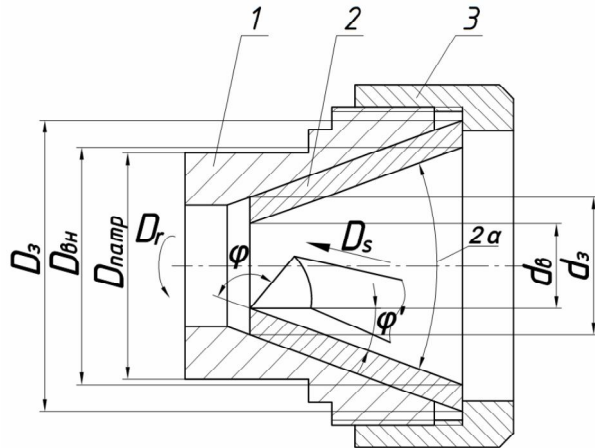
Схема розточування внутрішньої циліндричної поверхні зразка: 1 – оправка; 2 – дослідний зразок; 3 – накидна гайка
